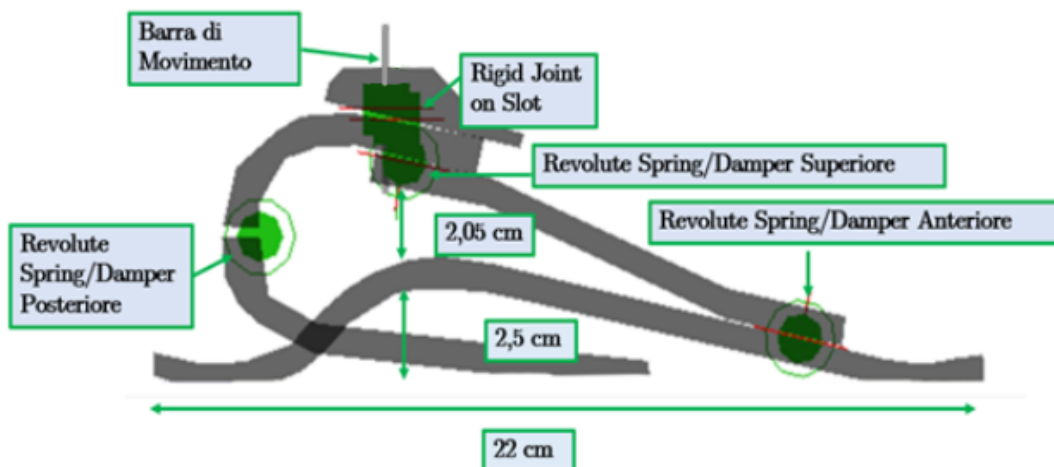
Disegno SimWise 4D piede protesico Walking Foot MP
